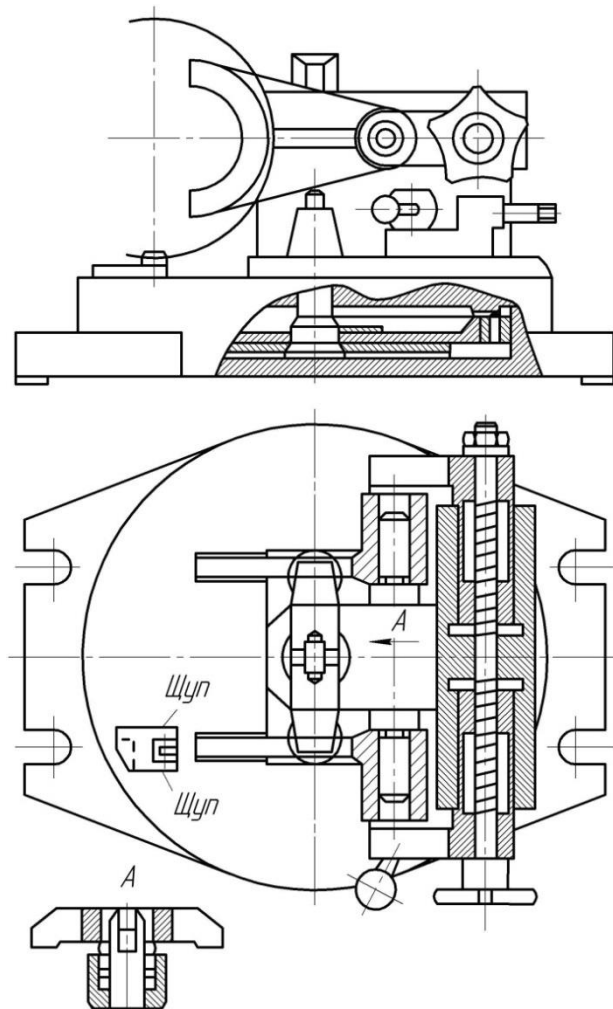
Схема пристосування для базування і закріплення двох плоских вилок і для координування фрези при фрезеруванні виконавчих поверхонь
